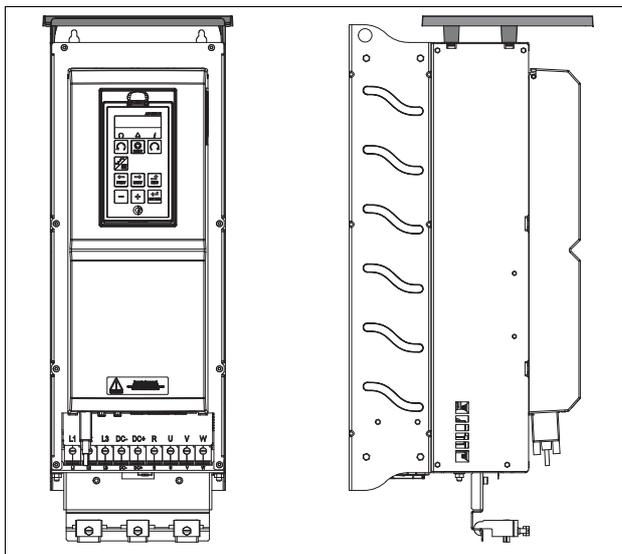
Дополнительная верхняя крышка, установленная на корпусе размера D2
